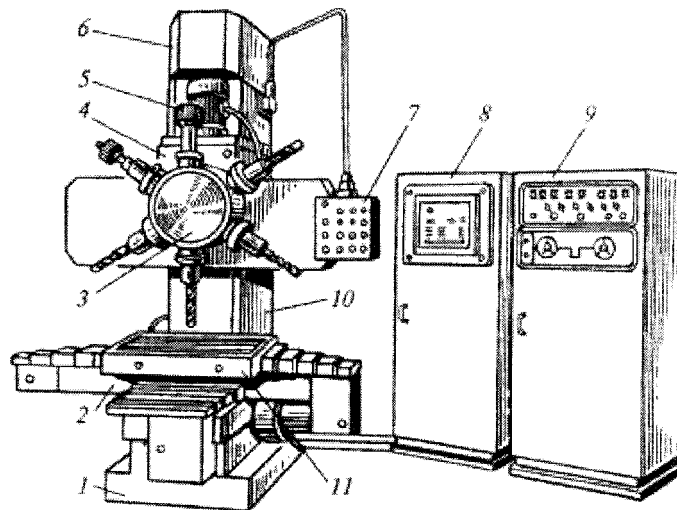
Вертикально-сверлильный станок с ЧПУ:
